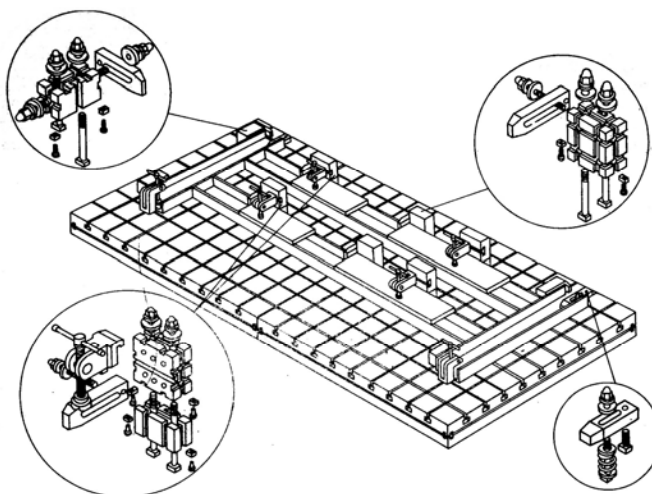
Общий вид компоновки УСПС для сборки рамной конструкции
